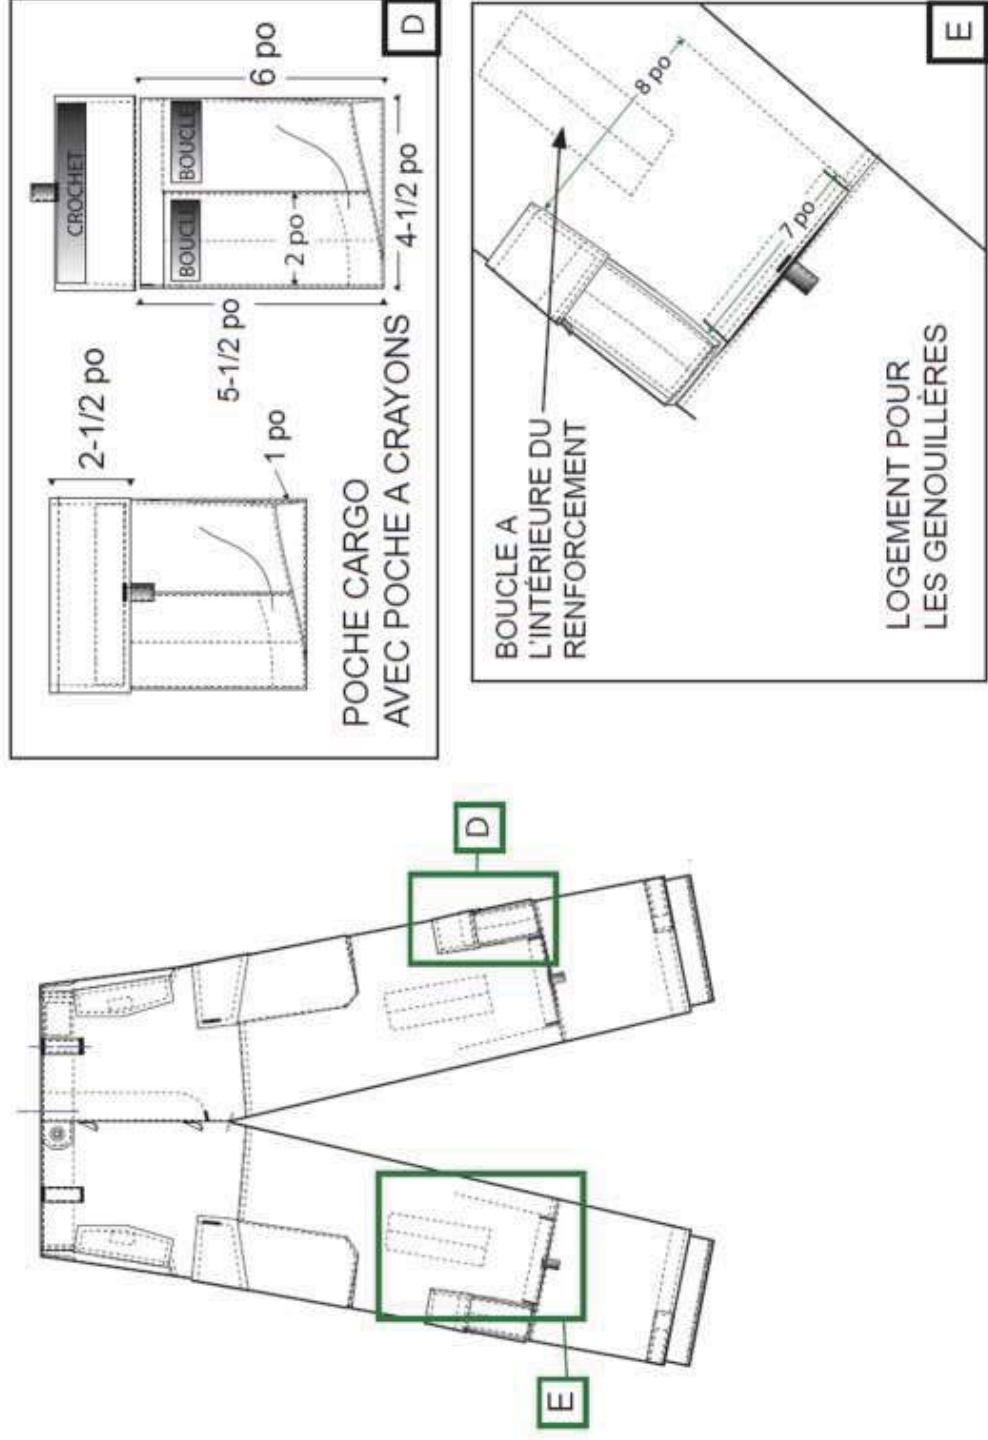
Dimensions des composants du vêtement - Vue du devant (con't)
